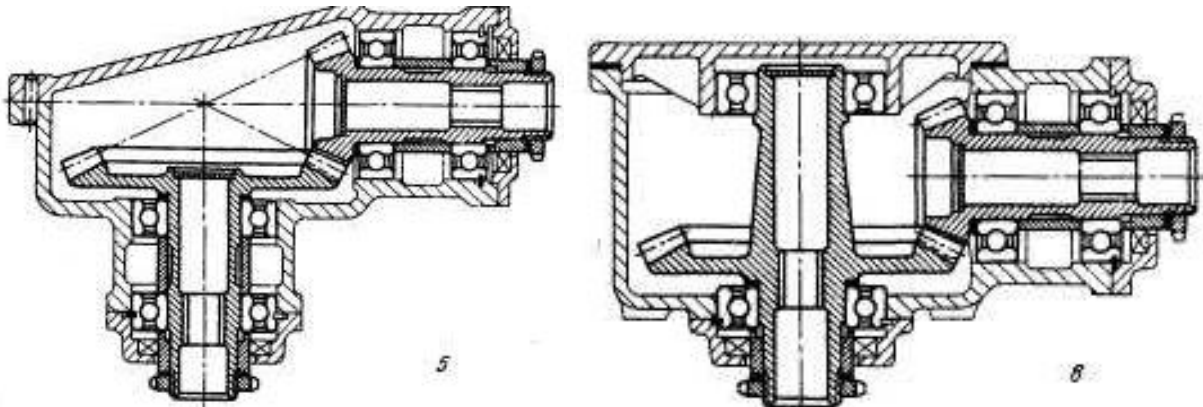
Варіанти 5 і 6 конструкції кутової передачі
